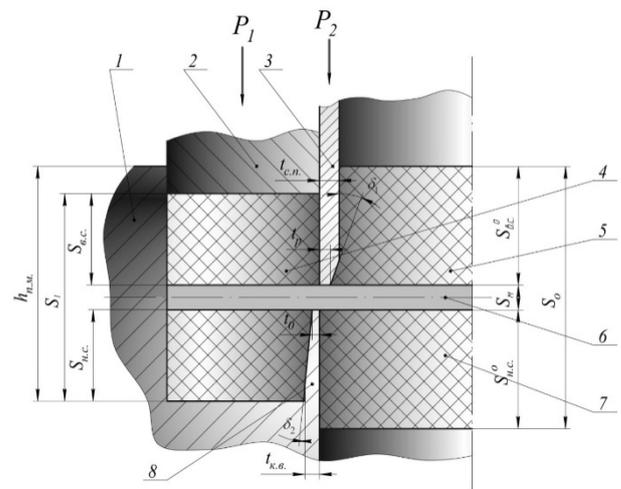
Схема разработанного способа пробивки отверстий в листовых многослойных заготовках с центральным металлическим слоем и утолщенными наружными эластичными слоями
